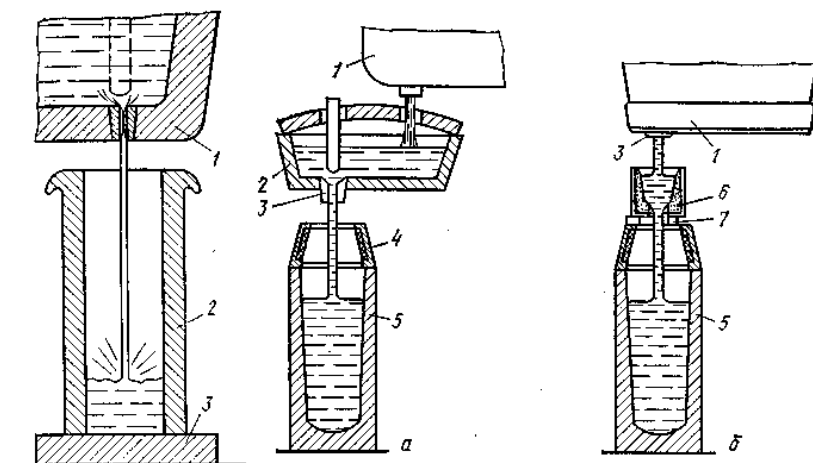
Схема разливки стали сверху, через промежуточный ковш (а) и промежуточную воронку (б)
